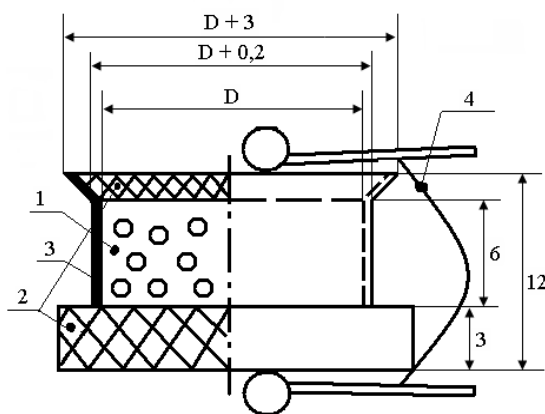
Сборка при подготовке образца: 1 – образец, 2 – фторпластовая подкладка, 3 – силиконовый слой, 4 – зажим, D – определяется после сушки образца
